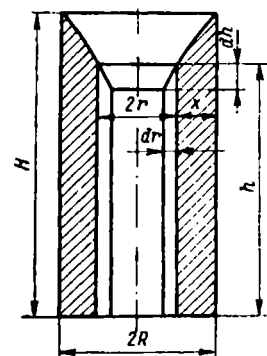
Схема к расчету усадочной раковины в цилиндрической отливке
